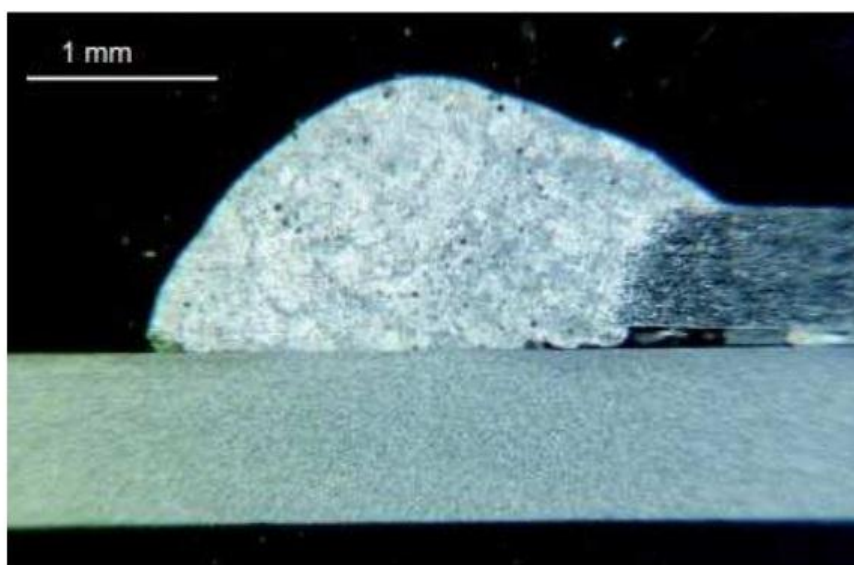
Макроструктура сварного соединения алюминиевого сплава AW-6016 и стали DP 600 (Z 140), выполненного ЭЛС в атмосфере. Присадочная проволока AlSi12.
